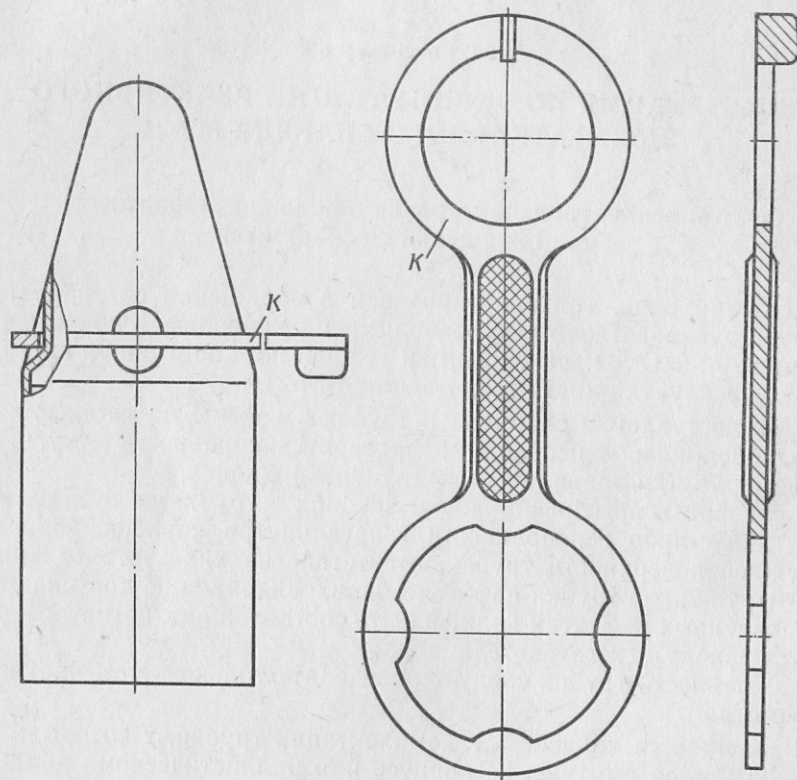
Схема снятия предохранительного колпака трубки ГДТ-90
